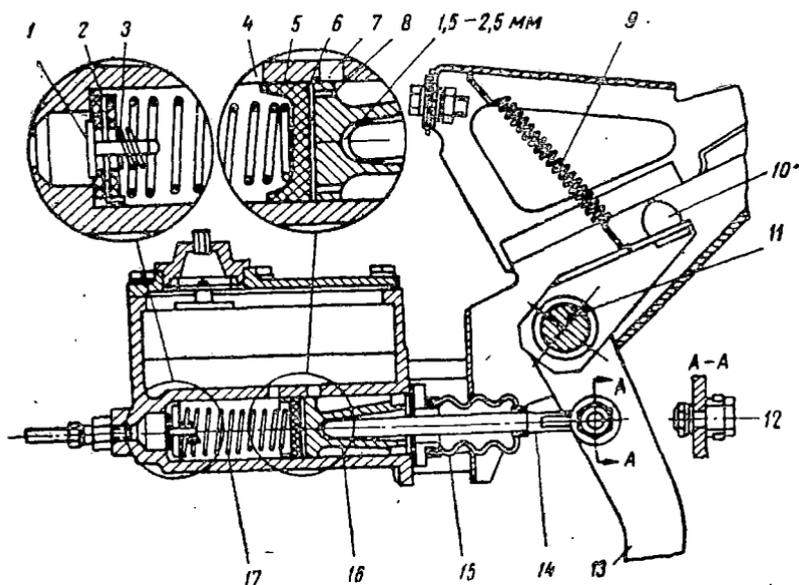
Главный тормозной цилиндр автомобиля ГАЗ-21 «Волга»:
